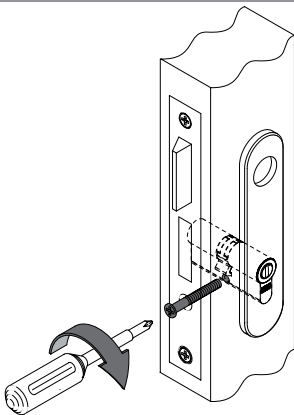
Batteriewechsel („Batteriewechsel“, Seite 16)
